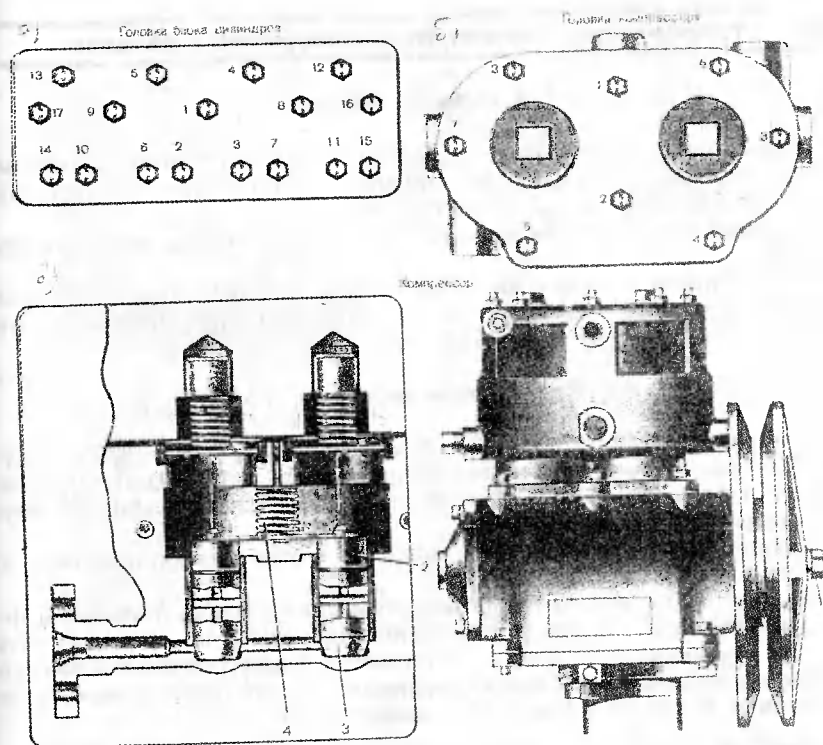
Головка блока (а); головка компрессора (б); компрессор (в): 1 — крепление шкива; 2 — гнездо штока; 3 — штуцер; 4 — пружина; 1—15 — последовательность подтягивания гаек крепления головки блока цилиндра; 1—8 — последовательность подтягивания гаек крепления головки компрессора
